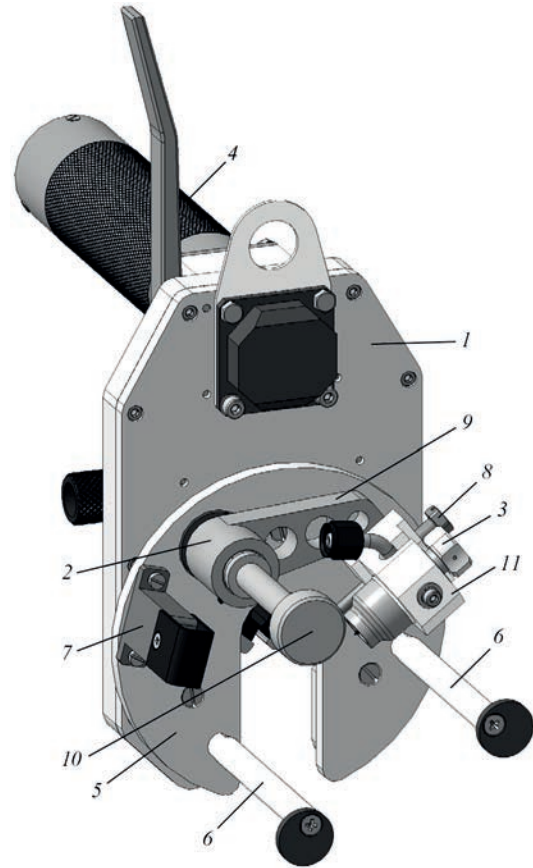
Общий вид головки сварочной АДЦ 627.03.00.000 (АДЦ 627.03.00.000-01) со стороны планшайбы (4 — рукоятка поляя, остальные обозначения см. в тексте)
